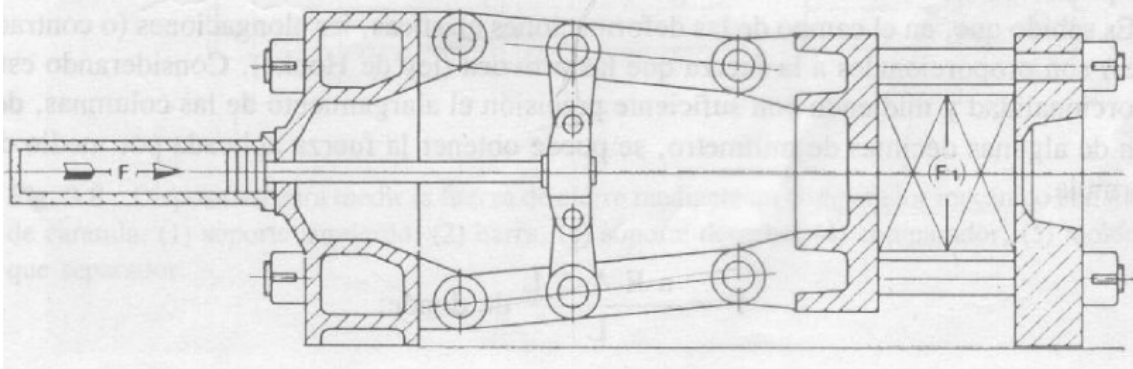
Cierre por rodillera doble con 4 puntos de unión.
